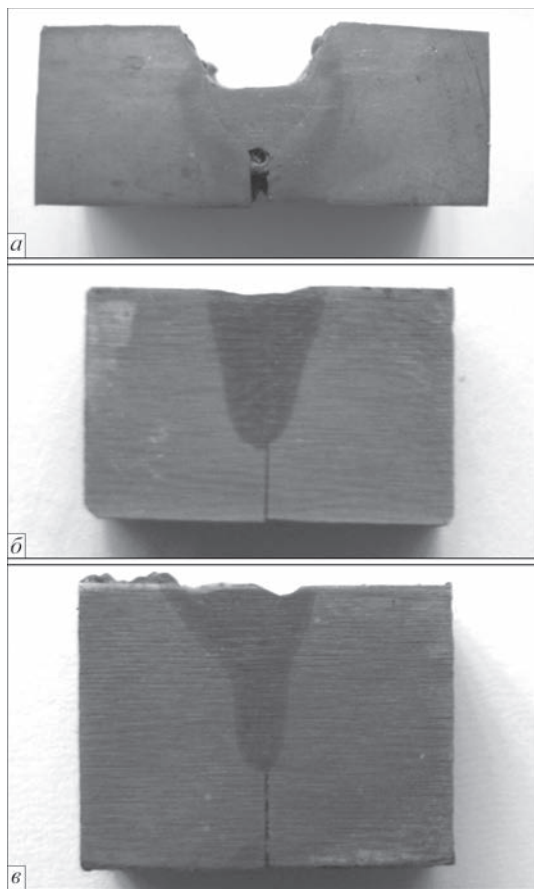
Макрошлифы из жестких стыковых технологических проб стали S460M толщиной 8 мм ($B = 100$ мм): *a* — при автоматической дуговой сварке в смеси газов Ar + 18 % CO₂ порошковой проволокой Megafil 821R ($v_{св} = 30$ м/ч (8,3 мм/с)); *б* — лазерной сварке без присадочного материала ($v_{св} = 40$ м/ч (11,1 мм/с)); *в* — при гибридной лазерно-дуговой сварке указанной выше порошковой проволокой ($v_{св} = 72$ м/ч (20,0 мм/с))
